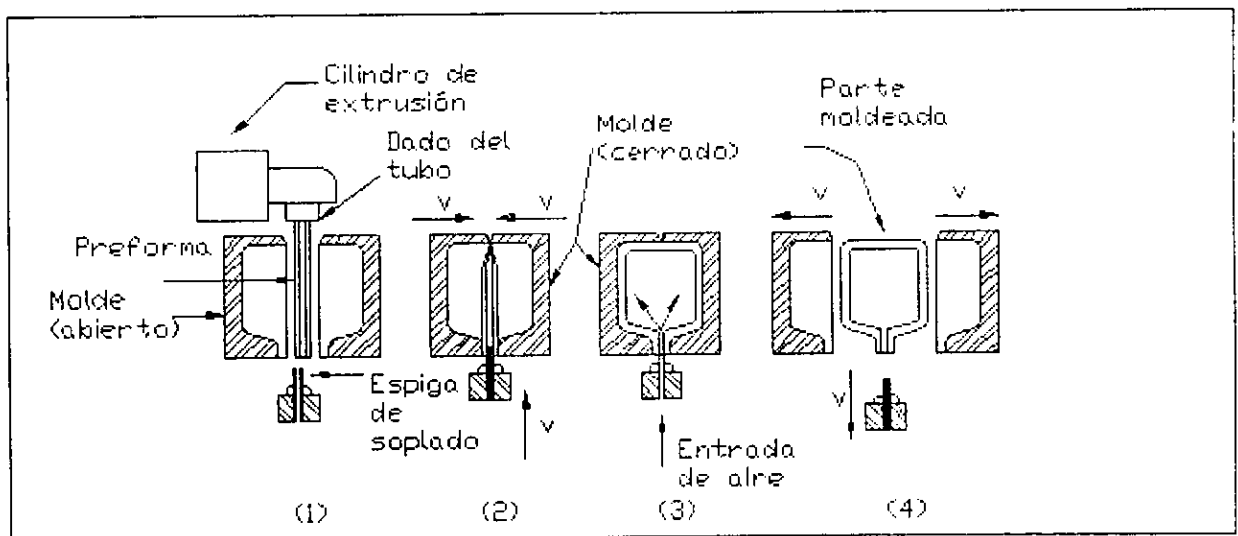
Moldeo por extrusión soplado: (1) extrusión de la preforma; (2) cuando se cierran las dos mitades del molde, la preforma se oprime en la parte superior y se sella en la parte inferior alrededor de una espiga de soplado; (3) el tubo se sopla y toma la forma de la cavidad del molde; y (4) se abre el molde para retirar la parte solidificada.
